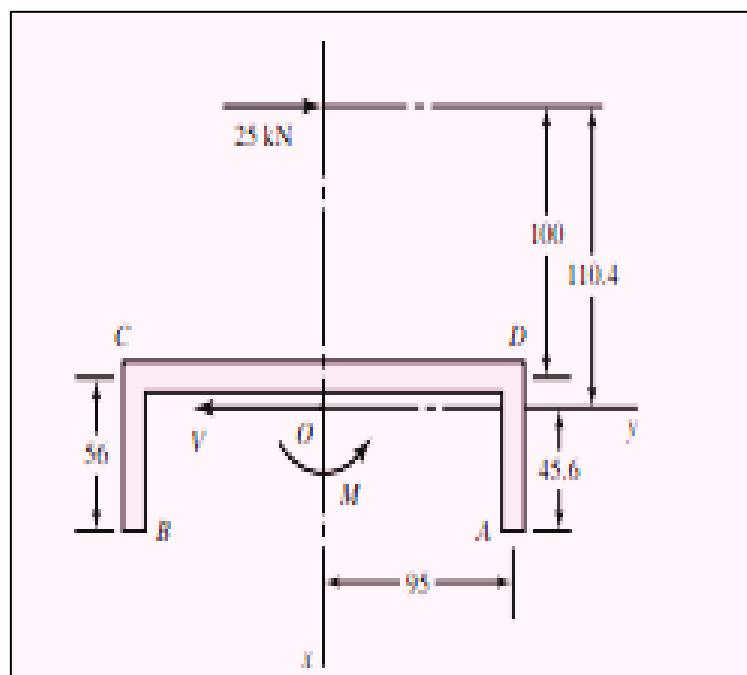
Diagrama de geometría de la soldadura. Extraído de Diseño en ingeniería mecánica de Shigley octava edición – 2008.
